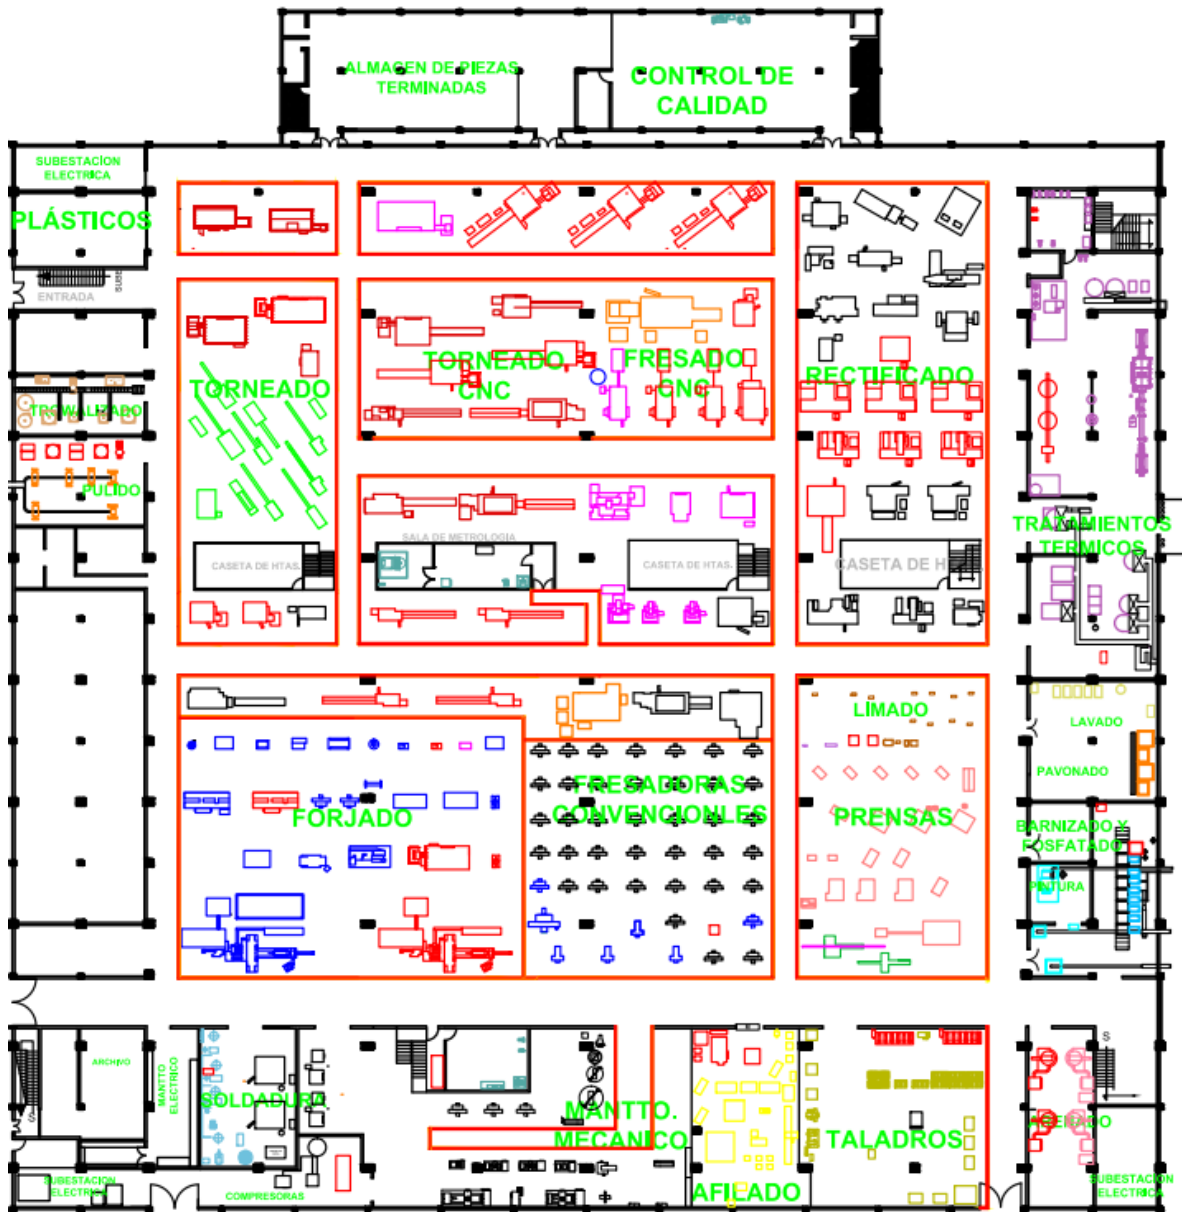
Distribución de planta actual de la fábrica de refacciones para armamento.
